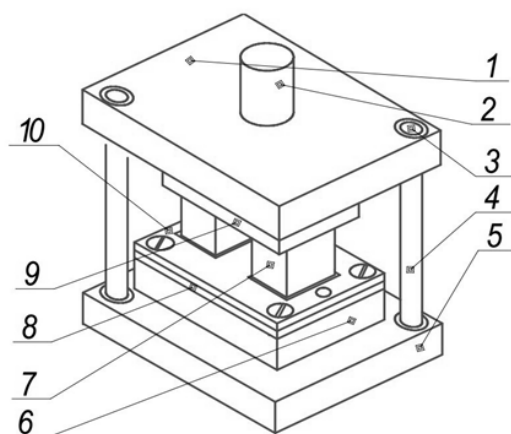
Принципиальная схема штампа [5]: 1 – верхняя плита; 2 – хвостовик; 3 – направляющая втулка; 4 – направляющая колонка; 5 – нижняя плита; 6 – матрица; 7 – пуансон; 8 – установочные детали; 9 – пуансонодержатель; 10 – съемник.
